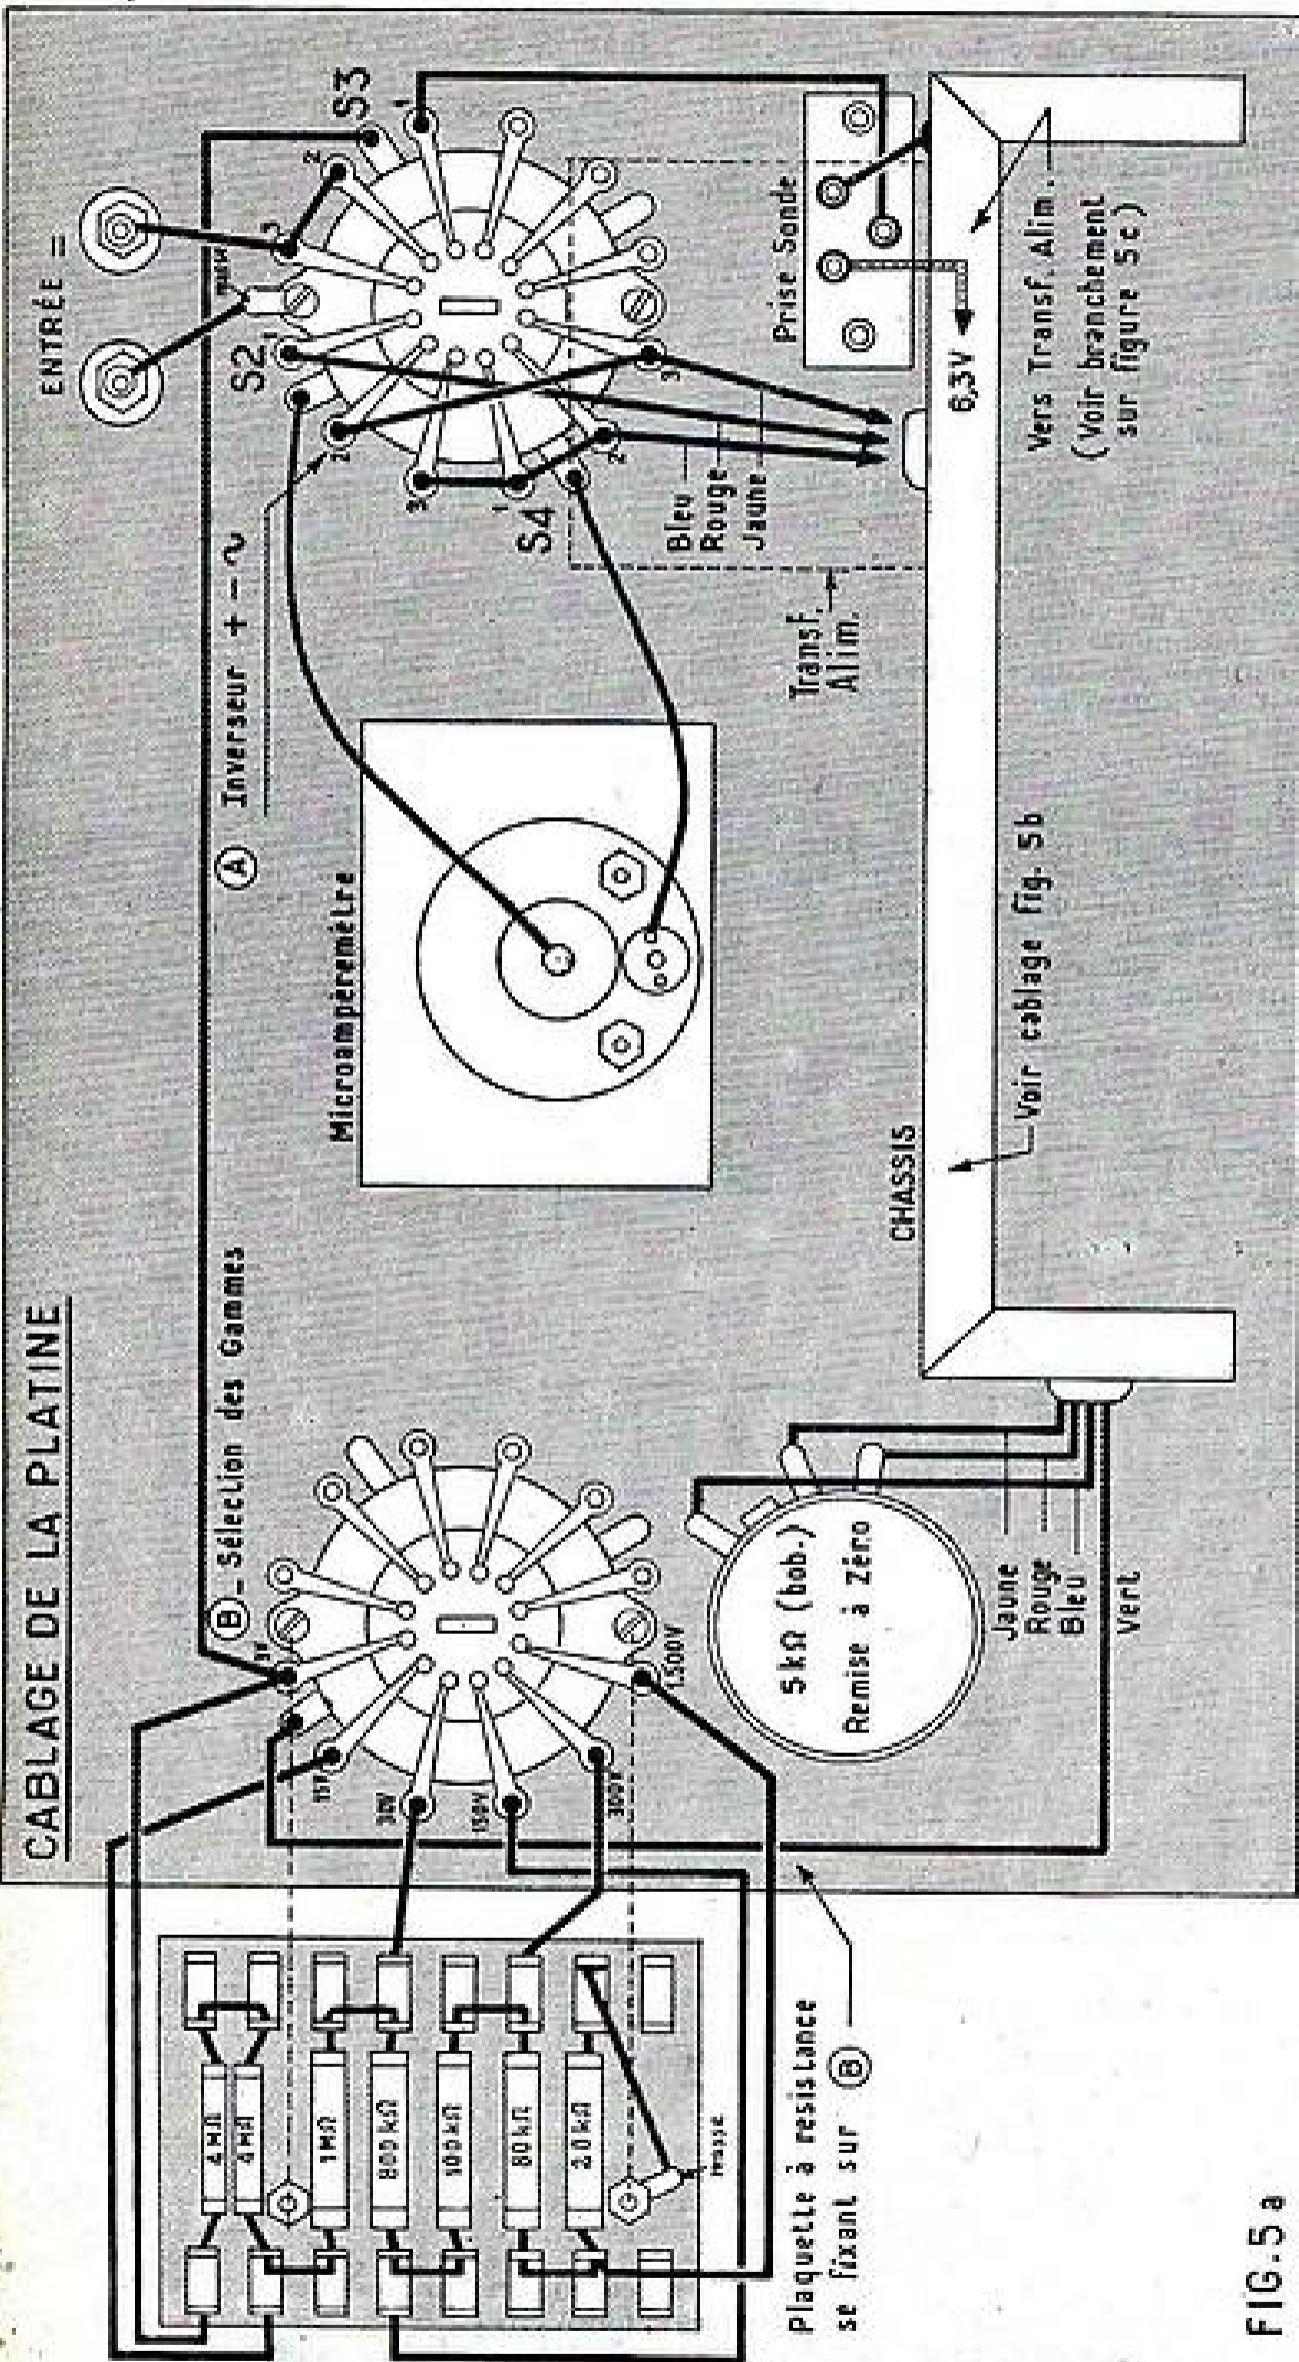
Plan de câblage de notre voltmètre et de la sonde.
